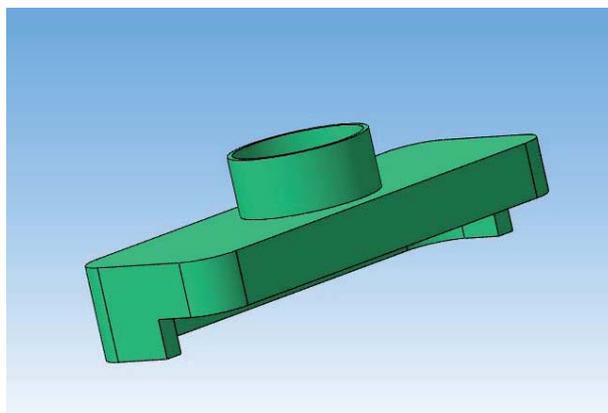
Внешний вид полимерного изделия «Деталь конструктора»
